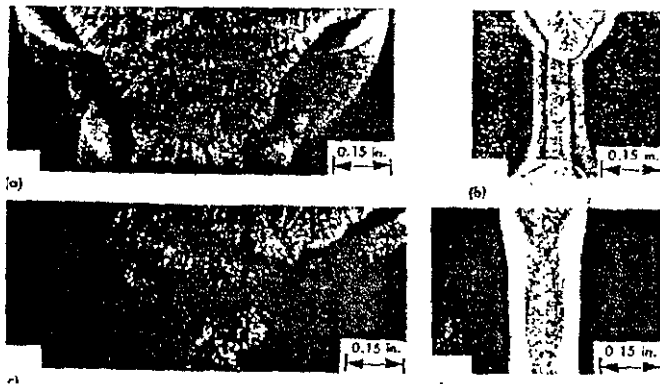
B Vista de la Sección trasversal de 0.5 mm NY-130 Soldadura realizada en 10% de amonio (a)soldadura de arco protegida (b)soldadura de haz de electrones (c) soldadura de arco en metal (d) soldadura de haz de láser.
